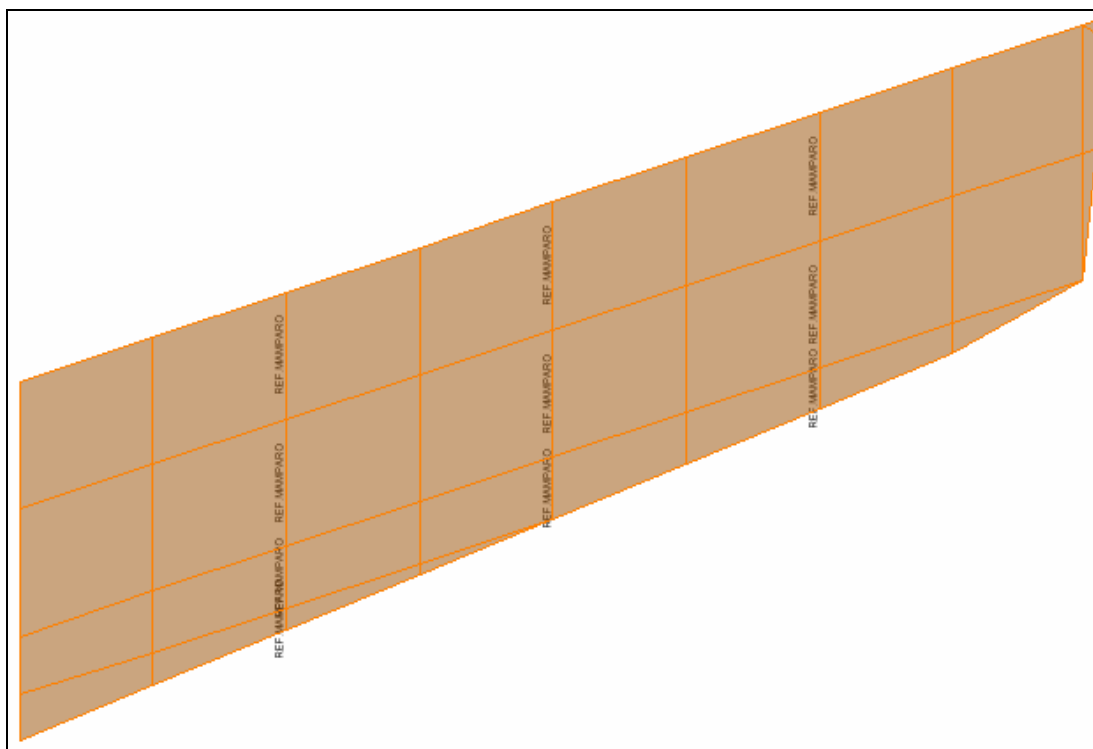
Detalle del mamparo y sus refuerzos verticales
